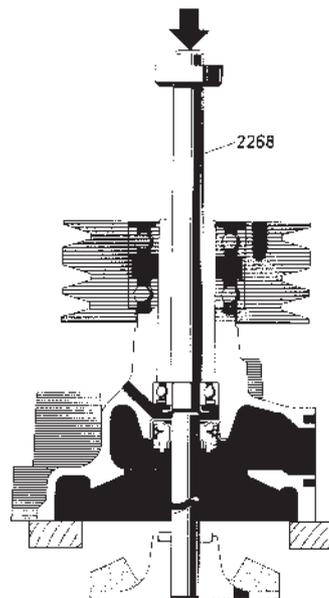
Démontage de la roue à aubes, des roulements et de la bague d'étanchéité
